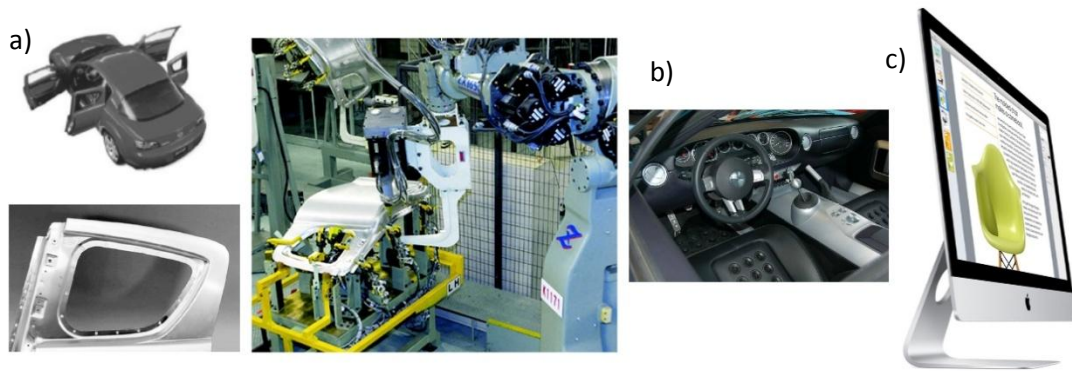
Aplicaciones en el mercado masivo. a) El automóvil Mazda RX-8 lleva soldadura FSW por puntos en la puerta trasera, robot automático soldando estas piezas [44]. b) En la construcción del Ford GT se utiliza la técnica de FSW para soldar el túnel central [43] c) En el nuevo iMac se utiliza FSW para unir las partes trasera y delantera del ordenador [39].
